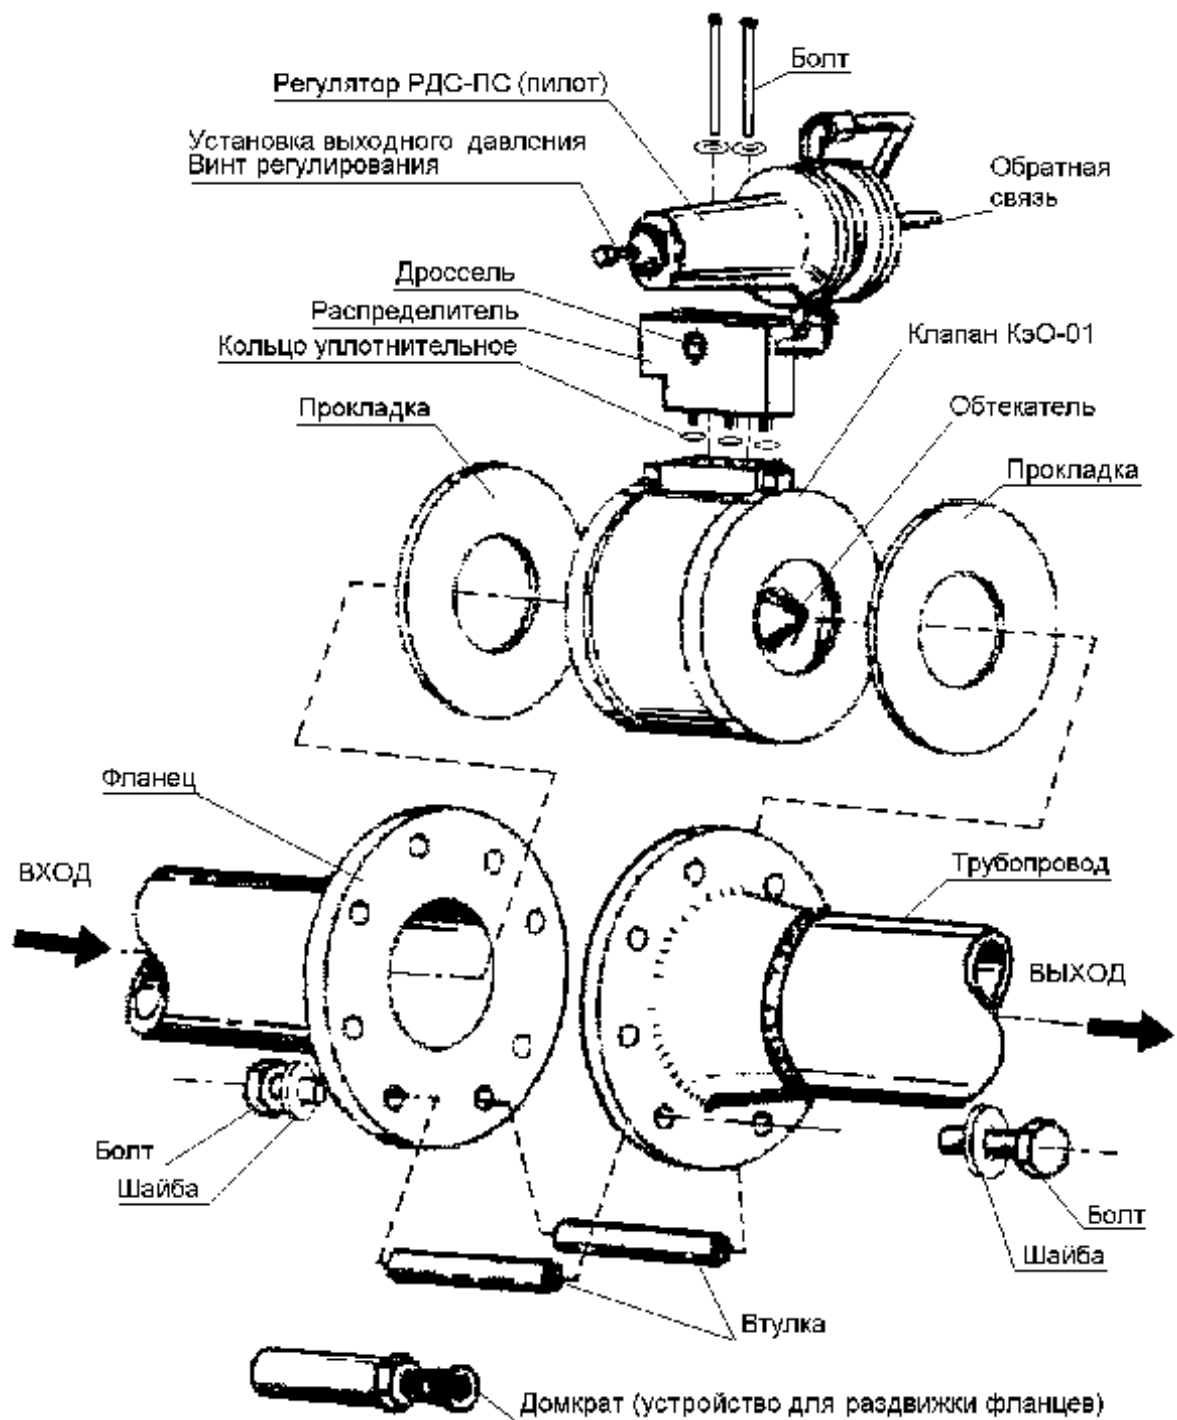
Схема монтажа регулятора РДО-1 на трубопроводе
